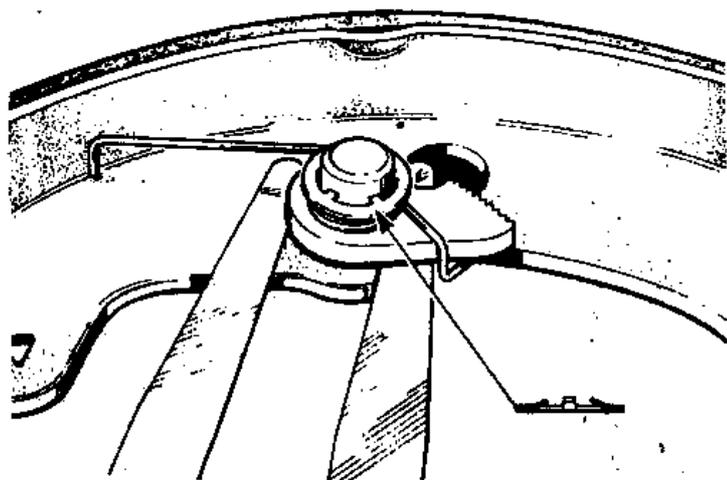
Установка на место короткого рычага храповика, пружины и шайбы (Разд.8)
